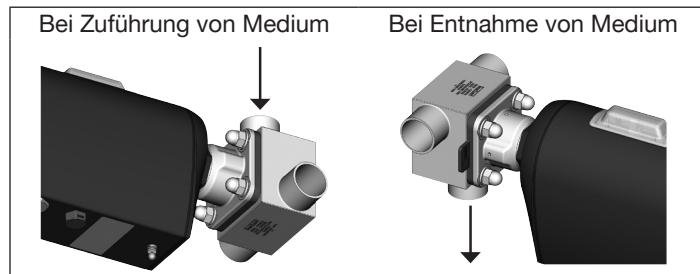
Einbaulage für T-Gehäuse, Typ 3324
